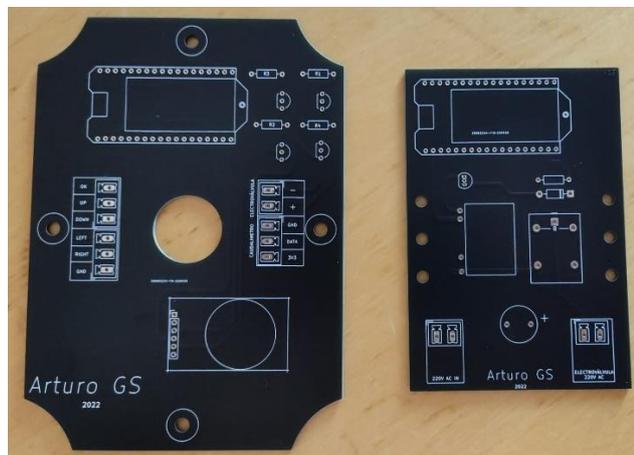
PCBs sin soldar. Fuente: elaboración propia.
